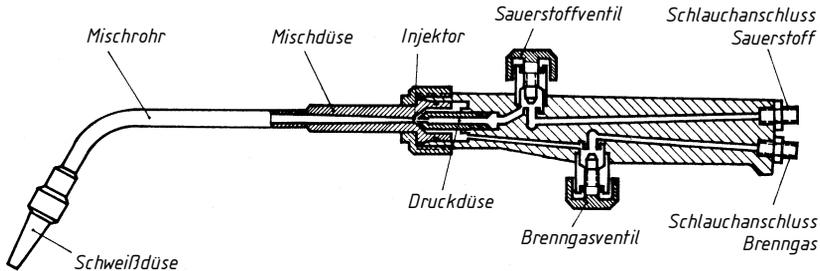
Schnittzeichnung eines Schweißbrenners nach dem Injektorprinzip. Der Injektor ist nicht verstellbar und gehört zum Brenneinsatz. Dazu ein komplettes Schweißdüsenset.
